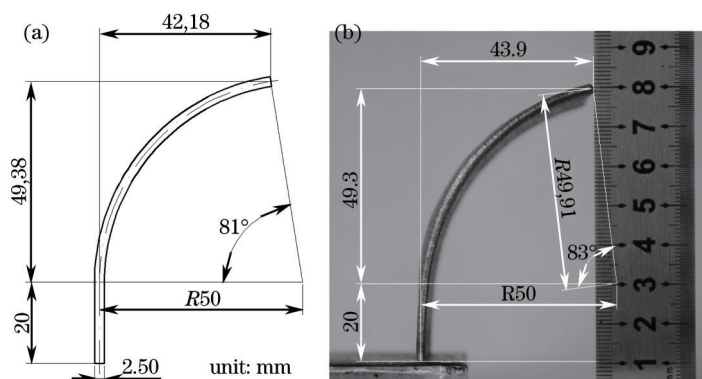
设计尺寸与成形件尺寸对比。(a) 侧面轮廓设计尺寸;(b) 成形件侧面轮廓尺寸测量
